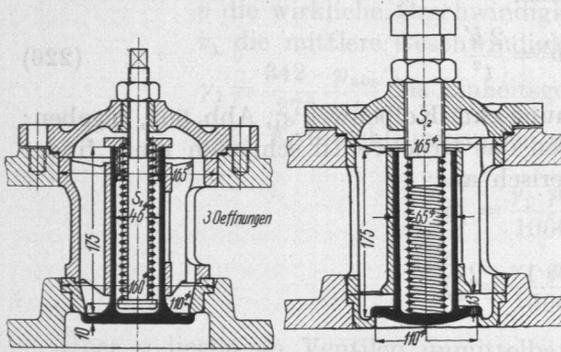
Saug- und Druckventil eines Kompressors (ältere Ausführung).
